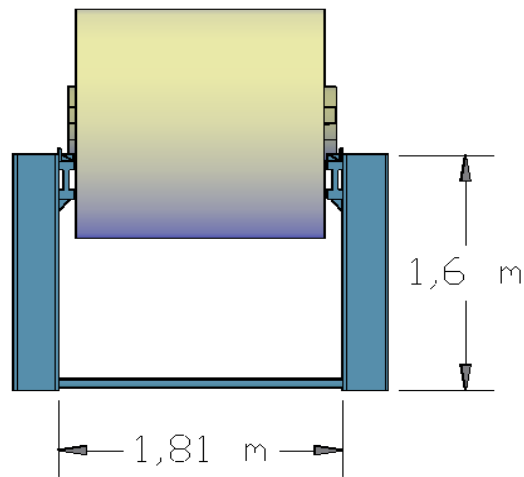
Dimensiones de Columnas de Apoyo
